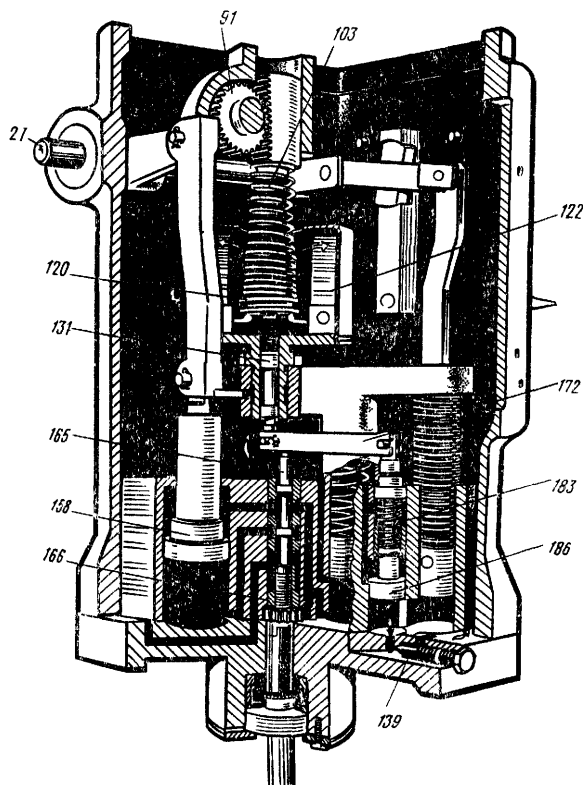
27— выходной вал; 91—вал-шестерня установки частоты вращения; 103 — задающая пружина; 120—муфта с подшипником; 122— грузы регулятора; 131—шток; 139—игла изодрома; 158—поршень сервомотора; 165—распределительный золотник; 166 — втулка распределительного золотника; 172—плавающий рычаг; 188 — пружина изодрома; 186 — принимающий поршень изодрома
